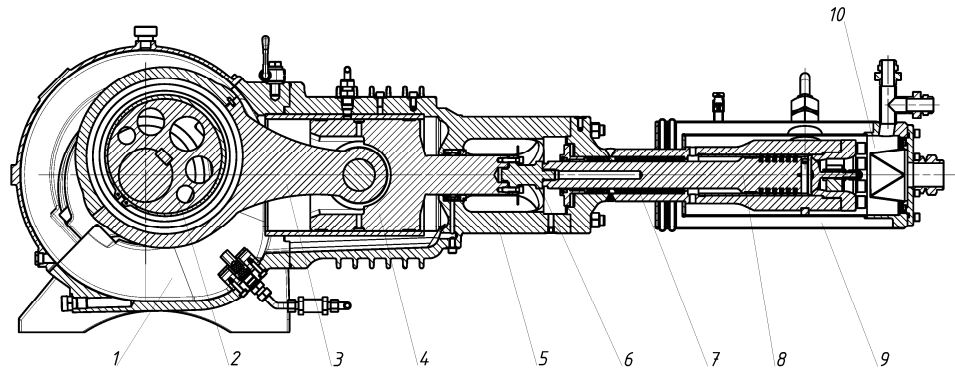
Газовий компресор високого тиску серії HPP3 60/110 фірми Cryostar. 1 – кривошипна камера; 2 – кривошип; 3 – шатун; 4 – крейцкопф; 5 – ущільнювальна камера; 6 – шток приводу робочого поршня; 7 – робочий циліндр із системою ущільнень; 8 – робочий поршень; 9 – вакуумна теплоізоляційна камера; 10 – прийомна камера
